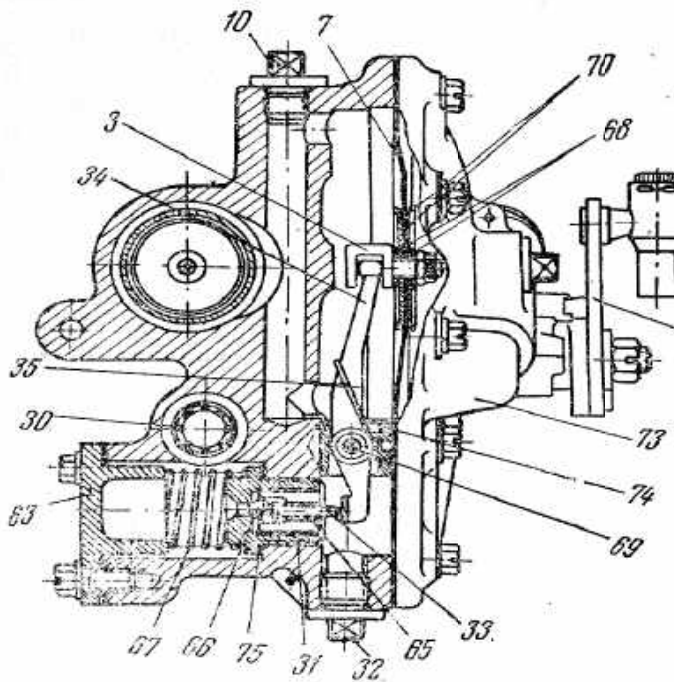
Мембранний механізм і паливний клапан: 3 – цапфа мембрани; 4 – важіль ручного керування коректором; 7 – мембрана; 10 – верхня зливна пробка; 30 – паливний фільтр; 31 – корпус паливного клапана; 32 – нижня зливна пробка; 33 – шток паливного клапана; 34 – важіль паливного клапана; 35 – пружина важеля паливного клапана; 63 – кришка паливного клапана; 65 – напрямна штока клапана; 66 – кулька; 67 – пружина; 68 – шайби; 69 – вісь важеля паливного клапана; 70 – диски мембрани; 73 – кришка мембранної камери; 74 – опора важеля; 75 – прокладка паливного клапана
